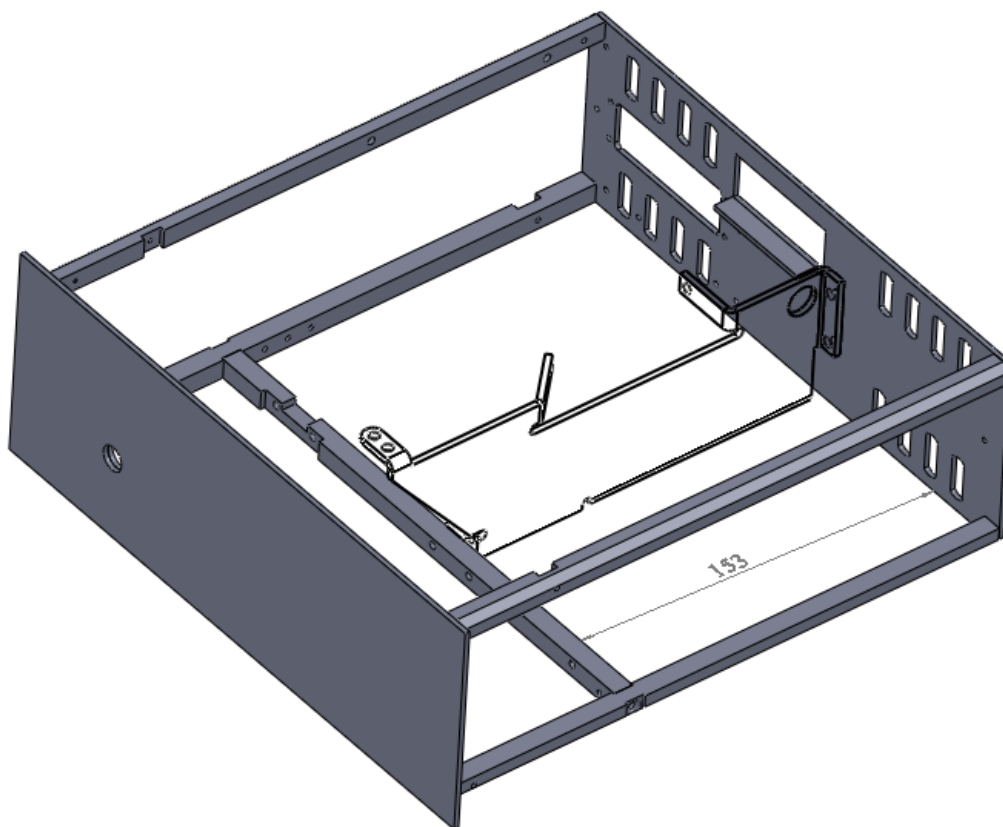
Трехмерная модель блока ЭС встраиваемой конструкции с определением базовой длины внутренней стенки
